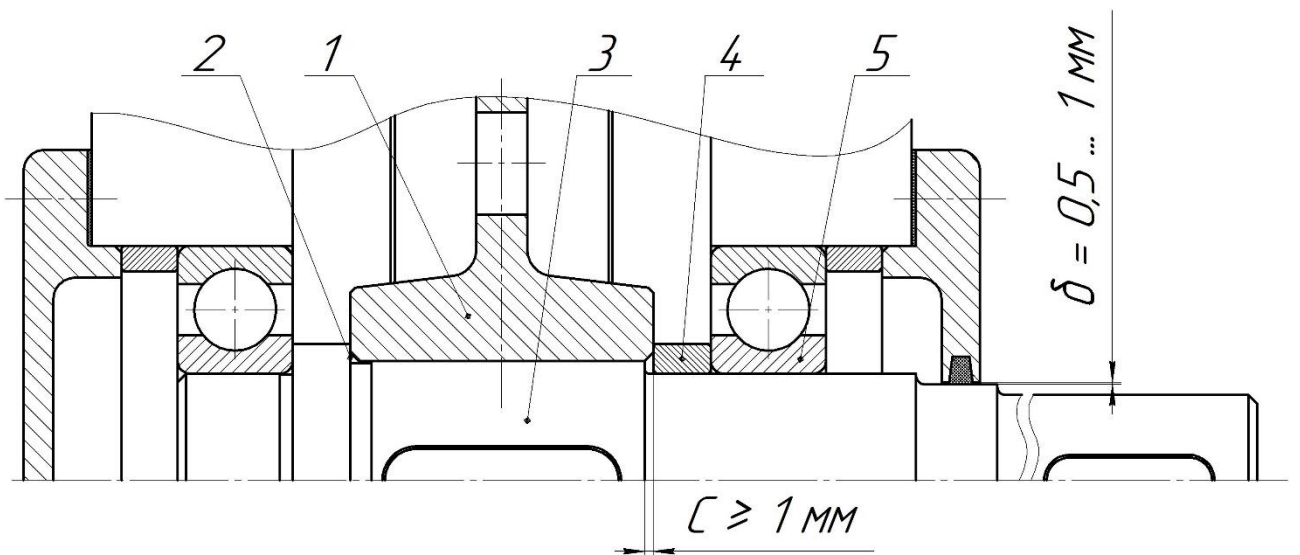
Схема к обоснованию конструкции вала и выбора зазора С
